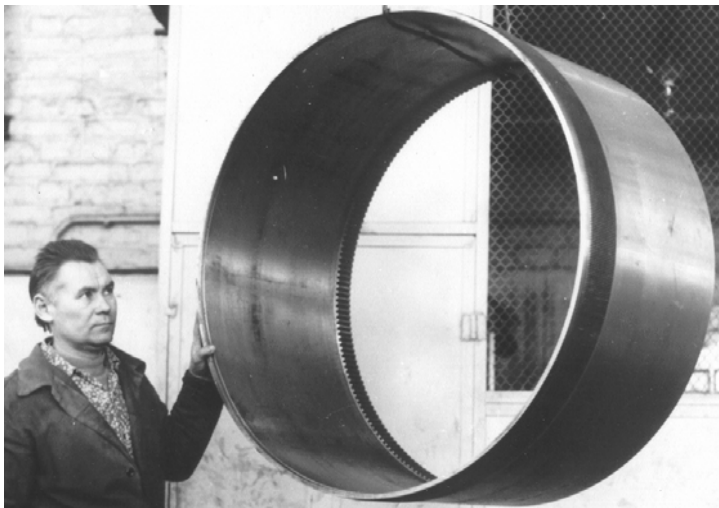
Гибкое колесо волнового редуктора поворота миксера МП-600АС
